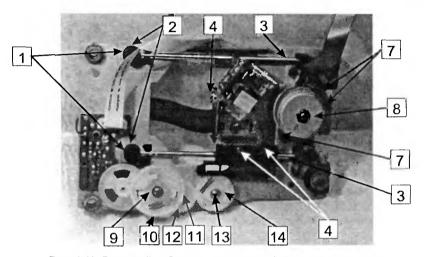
Внешний вид механизма привода дисков. Вид снизу
